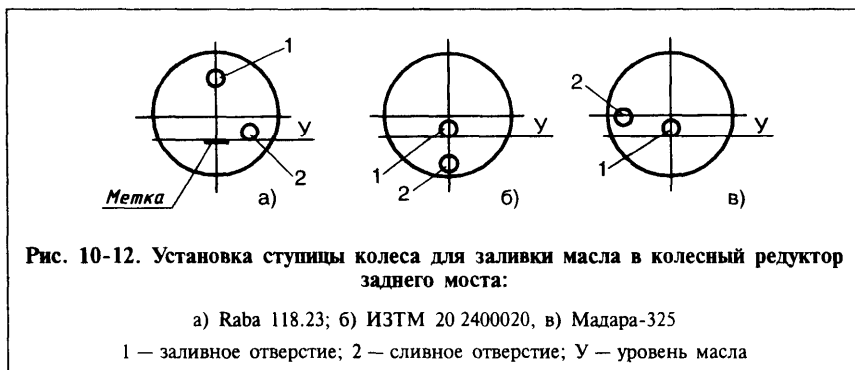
Установка ступицы колеса для заливки масла в колесный редуктор заднего моста:
